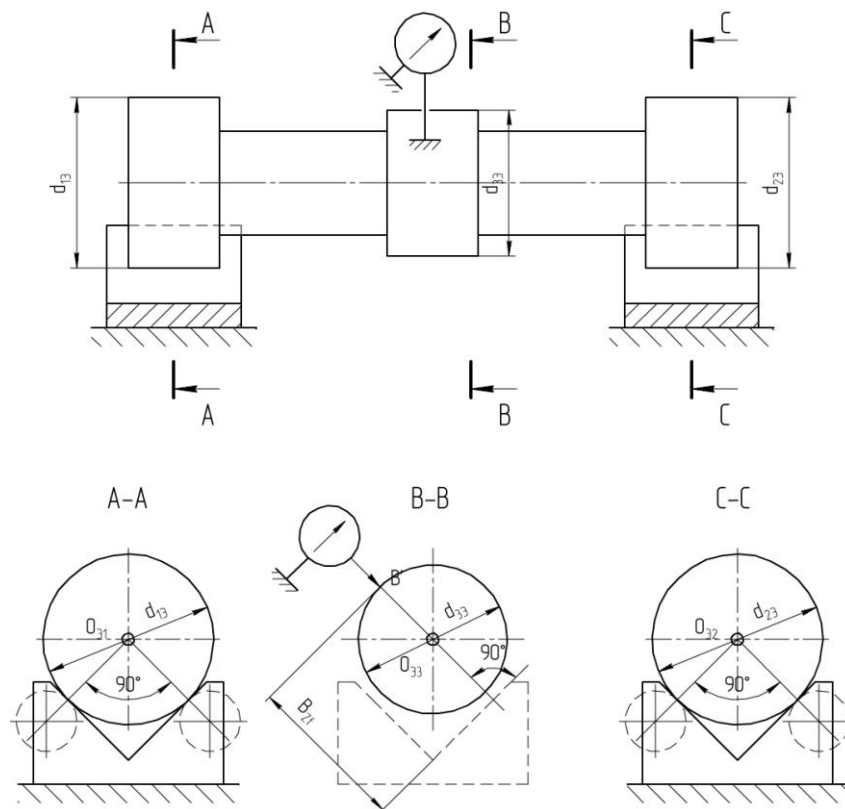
Схема контроля размера вхождения прилегающего профиля корпуса
